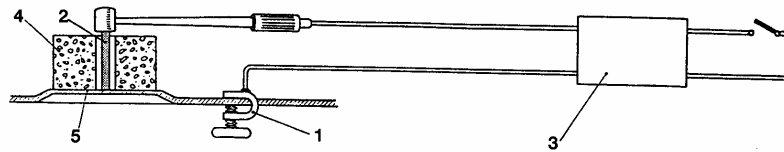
Esquema de la soldadora de puntos.
